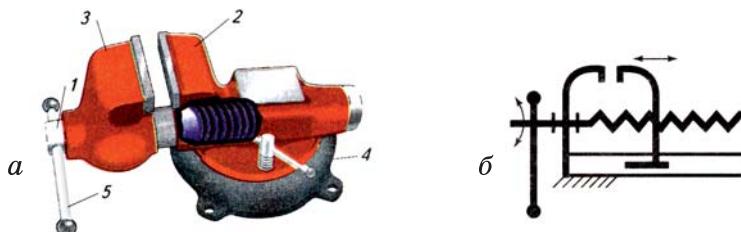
Тиски: а – устройство тисков (1 – винт, 2 – неподвижная губка, 3 – подвижная губка, 4 – опорная плита, 5 – рукоятка); б – схема тисков
